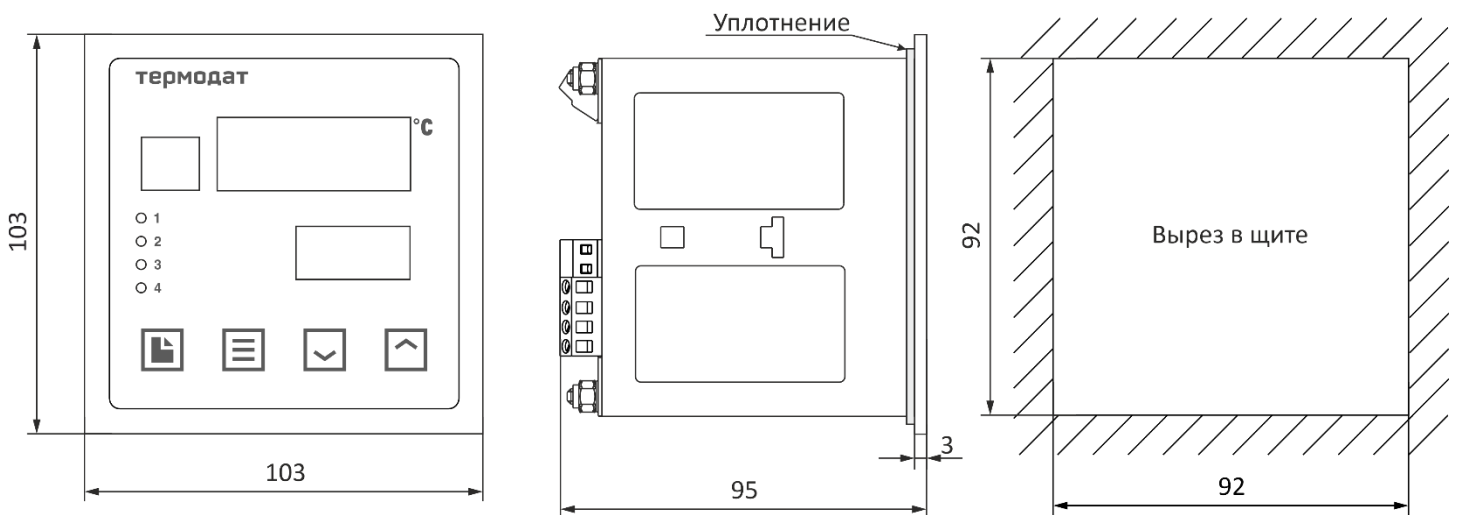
Габаритные размеры основного блока .../IP67пп
